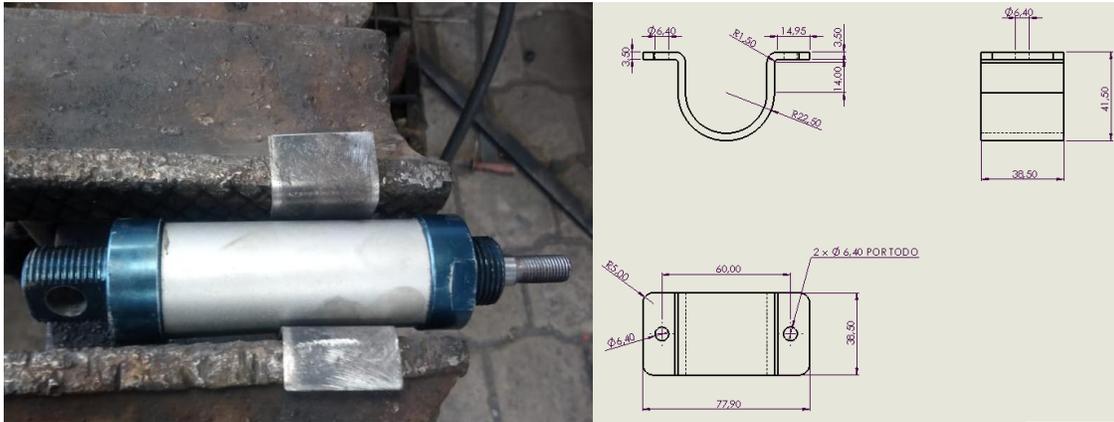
Construcción de elementos de sujeción para elementos desmontables
